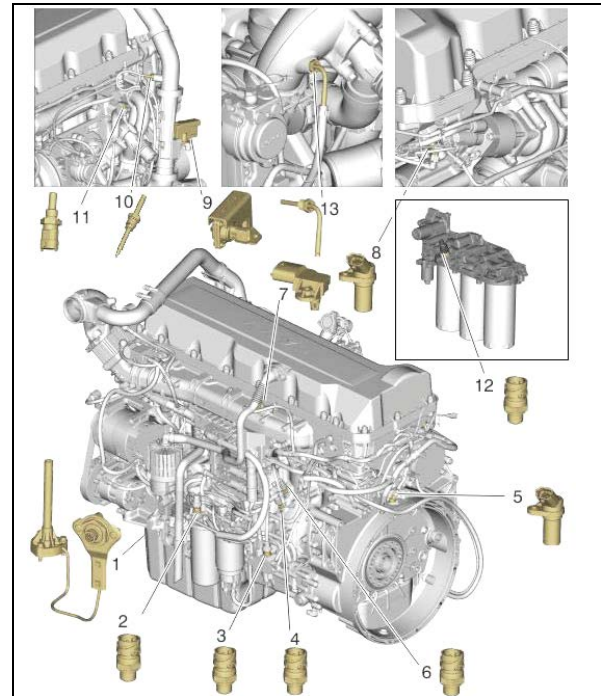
EMPLACEMENT DES CAPTEURS DU MOTEUR
